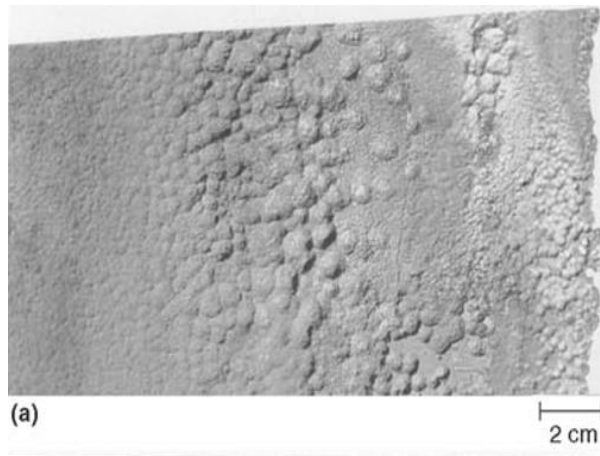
Ataque ocasionado por metal dusting sobre el acero tipo 310SS utilizado para la manufactura de fibras de carbono. Vista general (D. J. Young, 2007).
